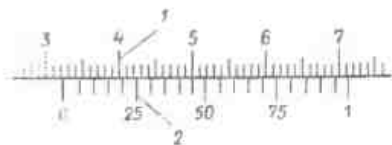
Отсчетное устройство штангенинструмента: 1 — основная шкала; 2 — шкала нониуса
